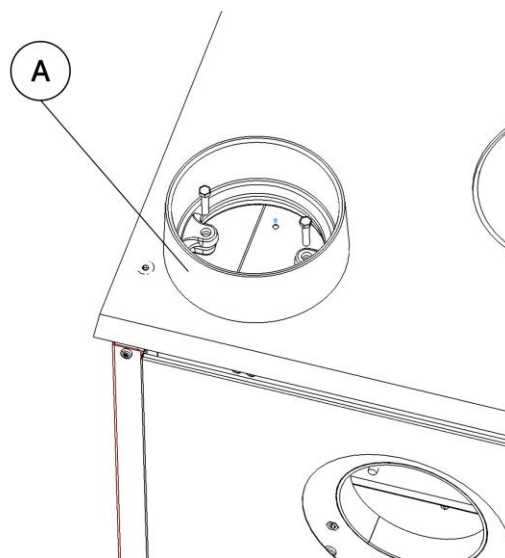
Colocamos a flange superior de saída de fumos.A
